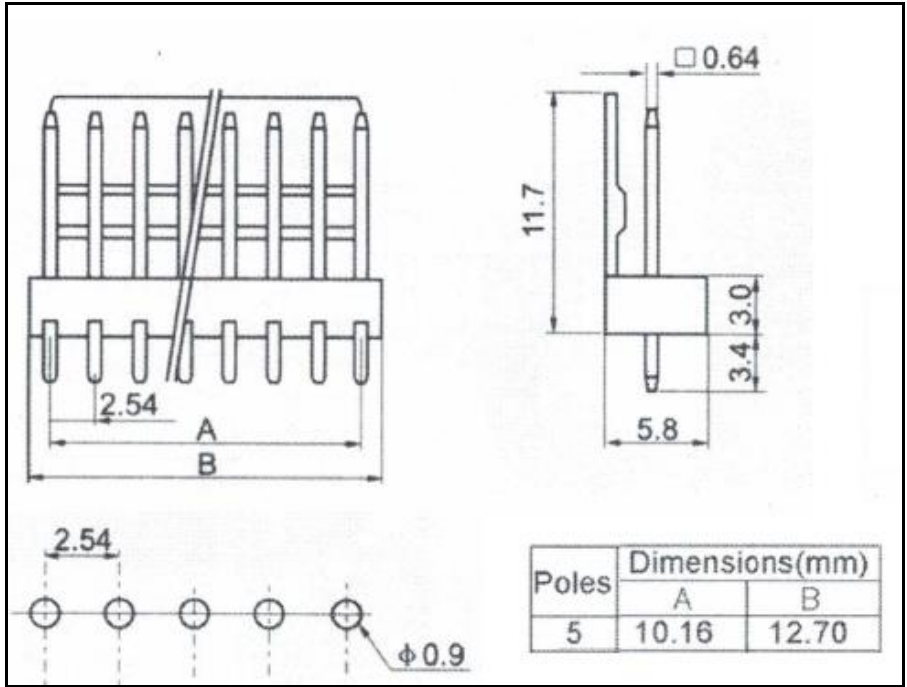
：焊接在 PCB 上的插座 J2 尺寸
